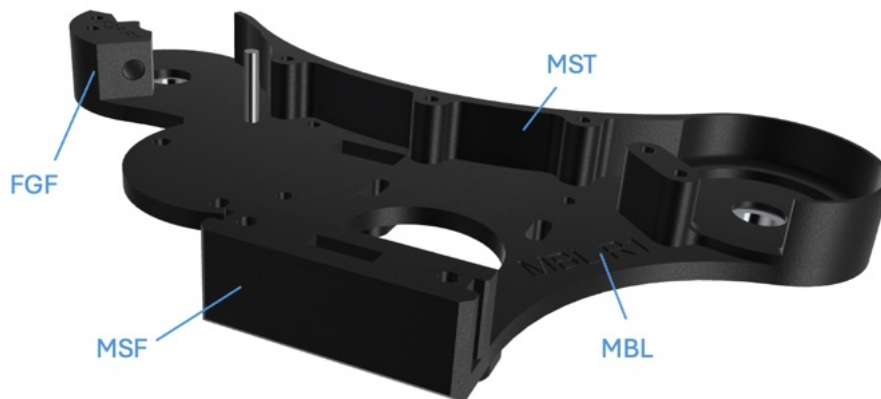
Rewinder-Chassis Montageschritt 2.
